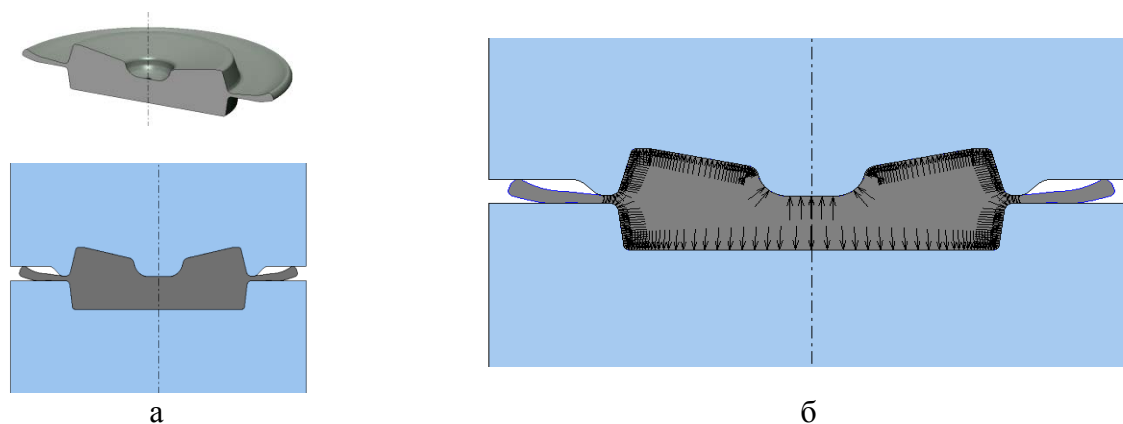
Штамповка поковки детали «Заборник» в открытом штампе:
